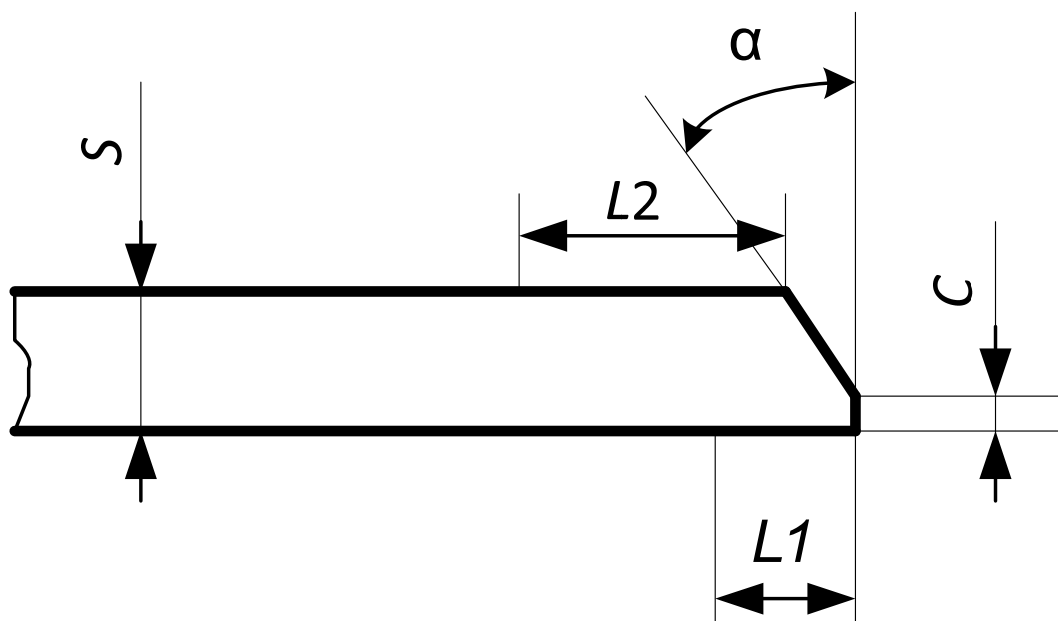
Эскиз контролируемого изделия при подготовке деталей под сварку (пластина)
